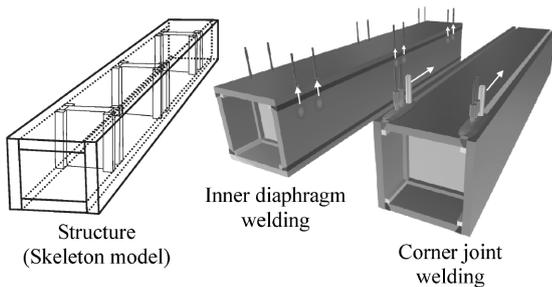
溶接組立箱形断面柱の構造と組立溶接法
